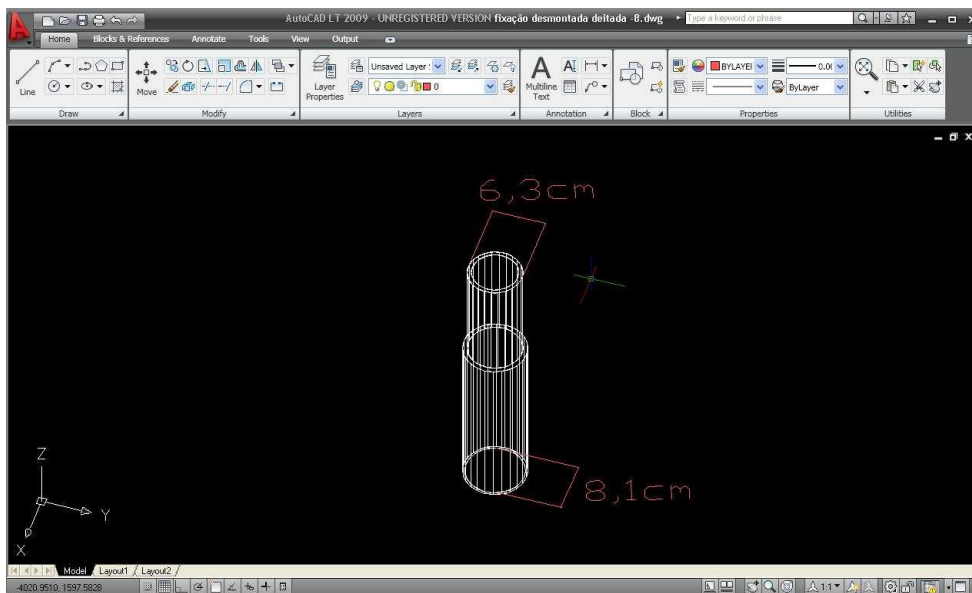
Desenho da peça de fixação do rotor ao mastro.
